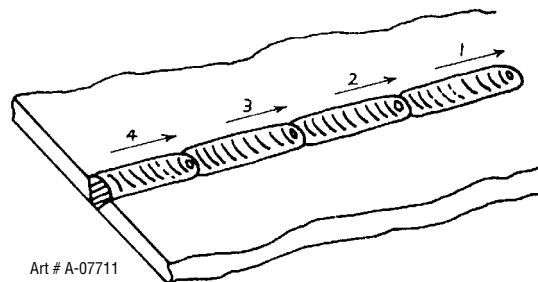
Pilgerschritt-Schweißen
